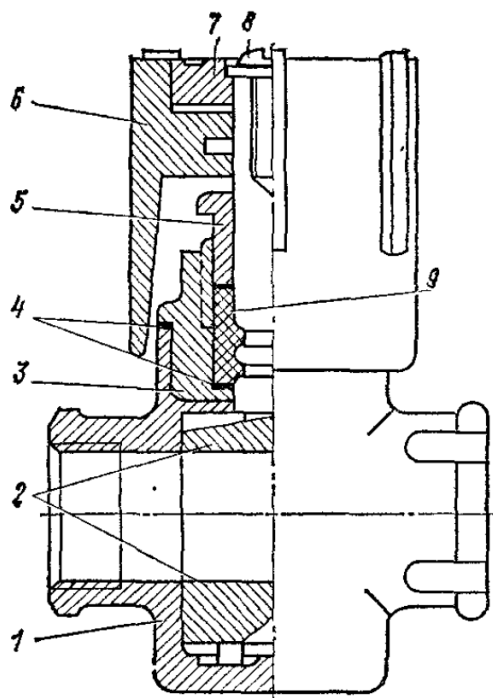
Край регулирующий трехходовой: 1 – корпус; 2 – заслонка; 3 – крышка; 4 – прокладки; 5 – гайка сальника; 6 – рукоятка; 7 – крышка-указатель; 8 – винт в шайбой; 9 – сальниковое уплотнение
